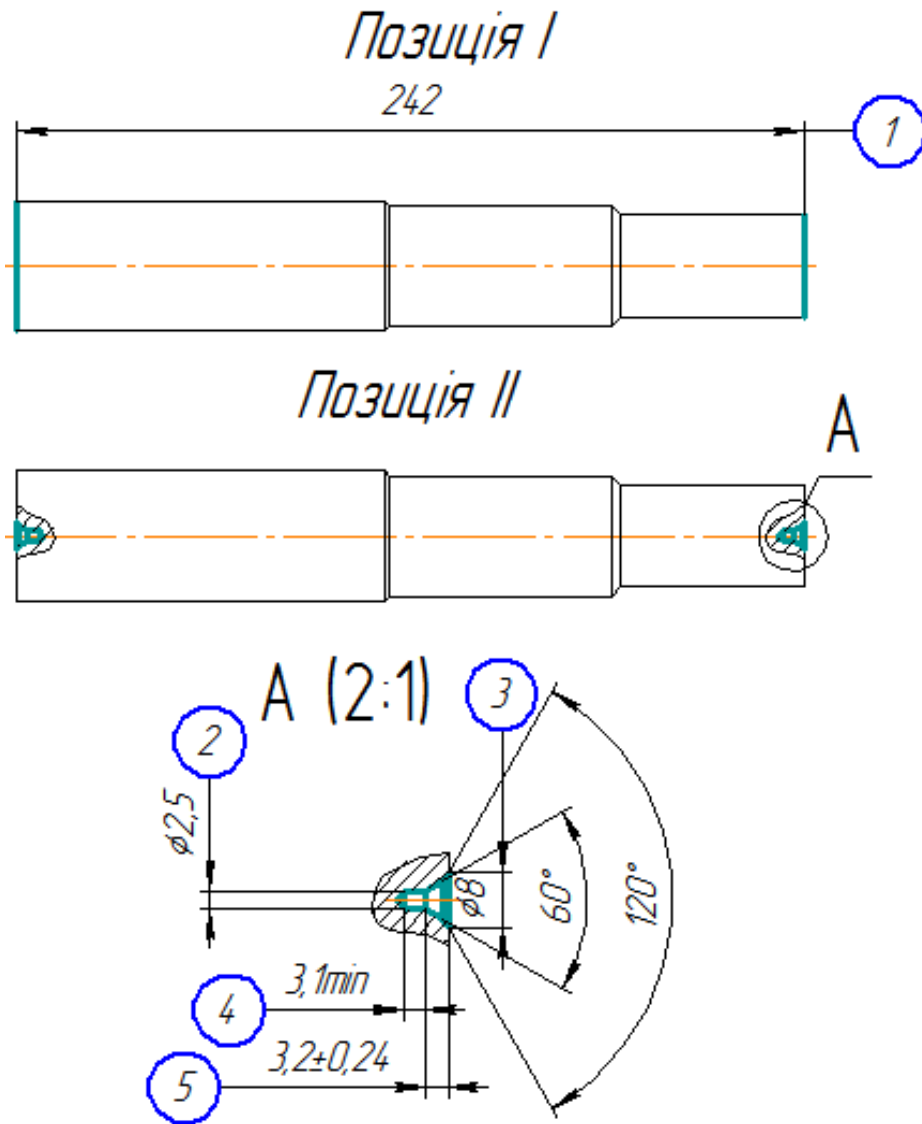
Ескіз обробки заготовки на операції 005
